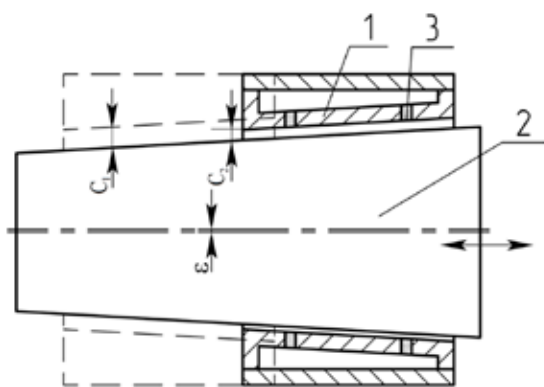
Газостатическая опора малой конусности: 1 – корпус подшипника, 2 – ротор, 3 – пористая вставка
